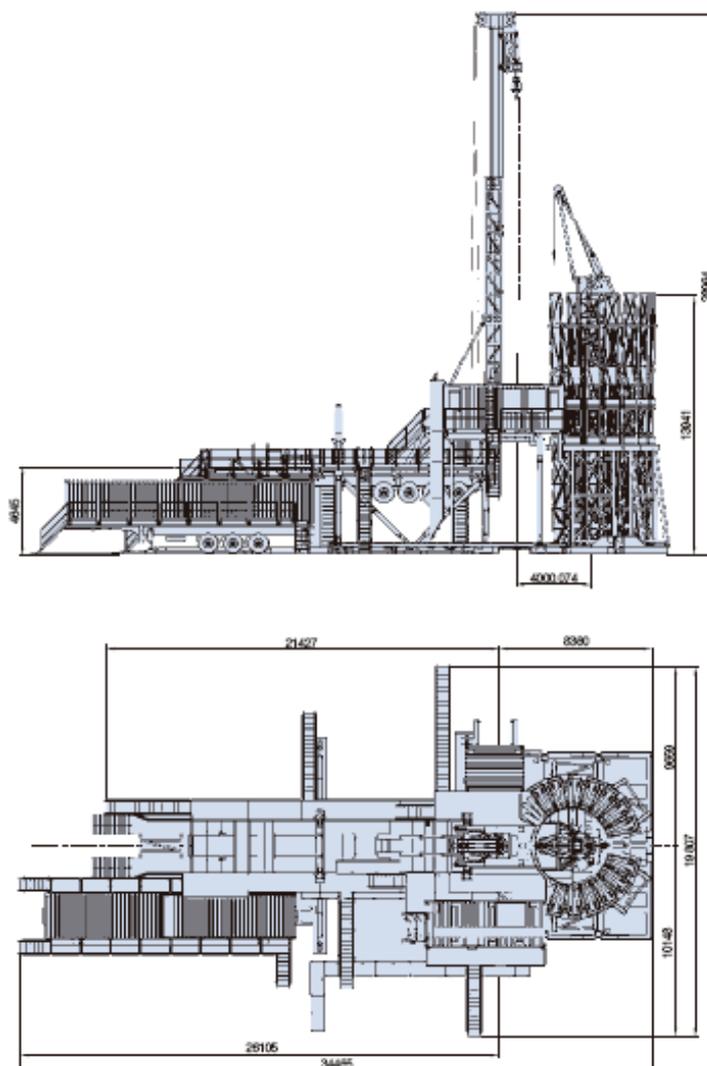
a – Impianto HH220 “Archimede” (pozzo Stogit Ripalta 62 Or)
